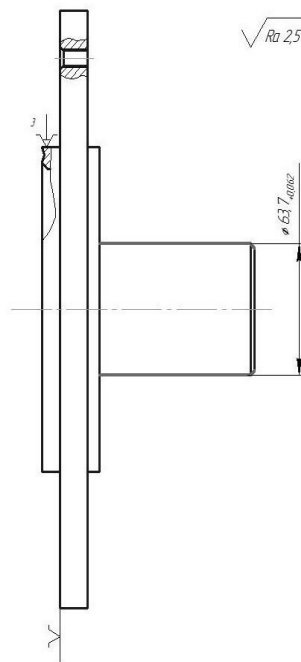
Фланець ведучої частини маточини колеса
